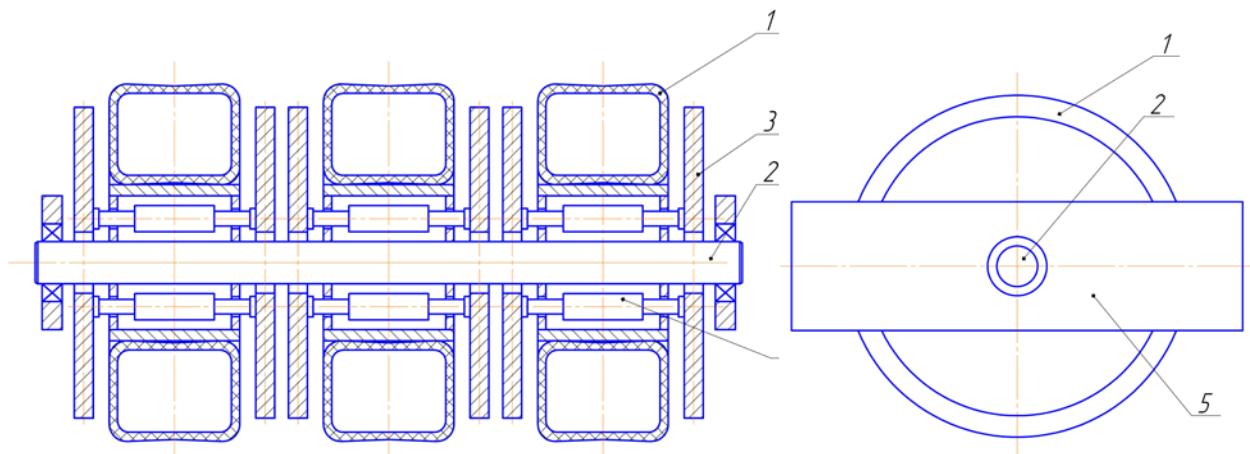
Вибрационный пневмошарнирный валец с торцевыми подвижными дисками
